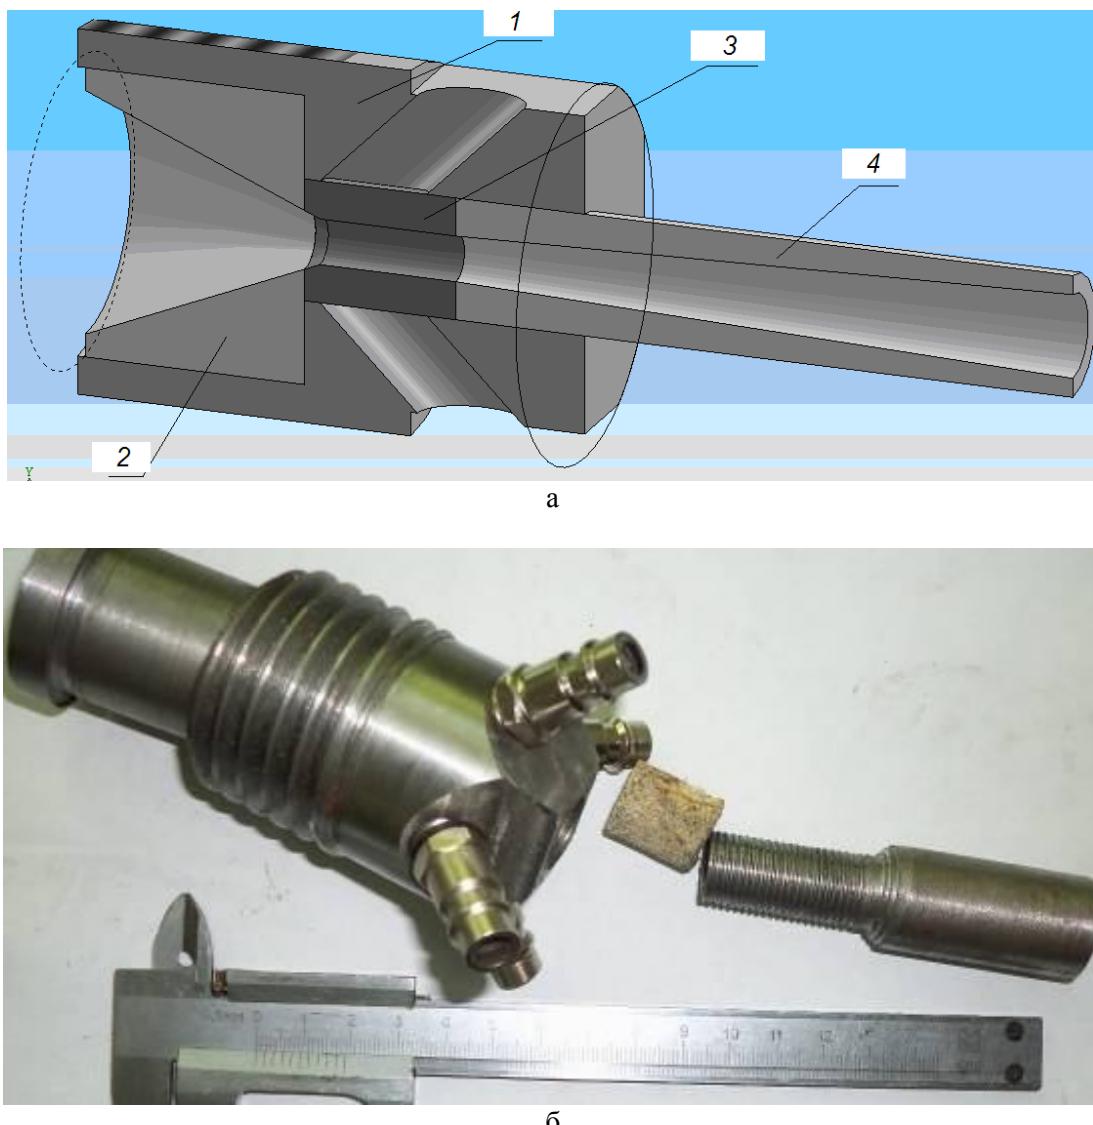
Готова збірна одиниця сопла нової конструкції. а – САПР модель збірної одиниці сопла (1 – корпус; 2 - широкий конічний вхід; 3 - пориста циліндричні трубчаста вставка; 4 - вузький довгий конічний вихід); б – реально виготовлена збірна одиниця сопла.
